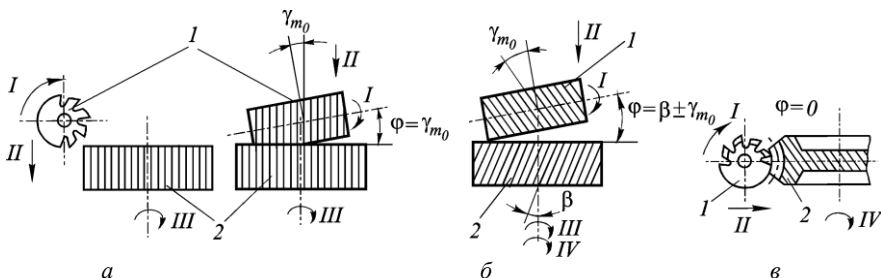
Схемы работы червячной модульной фрезы: а – при нарезании цилиндрических прямозубых колес; б – при нарезании цилиндрических колес с винтовым зубом; в – при нарезании червячных колес; 1 – фреза; 2 – заготовка
